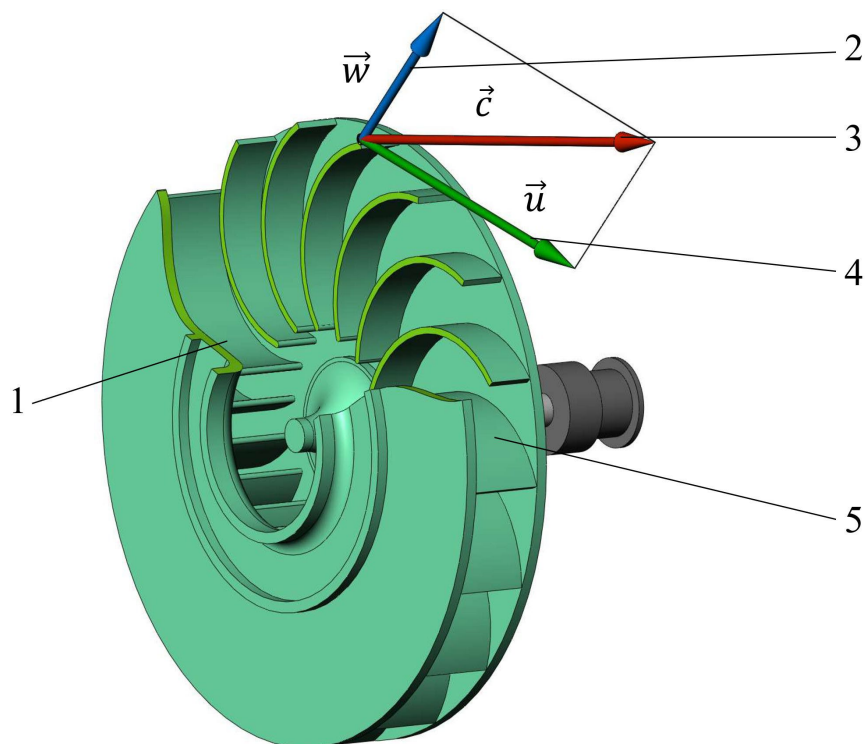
Конструкція робочого колеса із загнутими вперед лопатками
